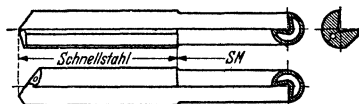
Tieflochbohrer neuerer Ausführung.
